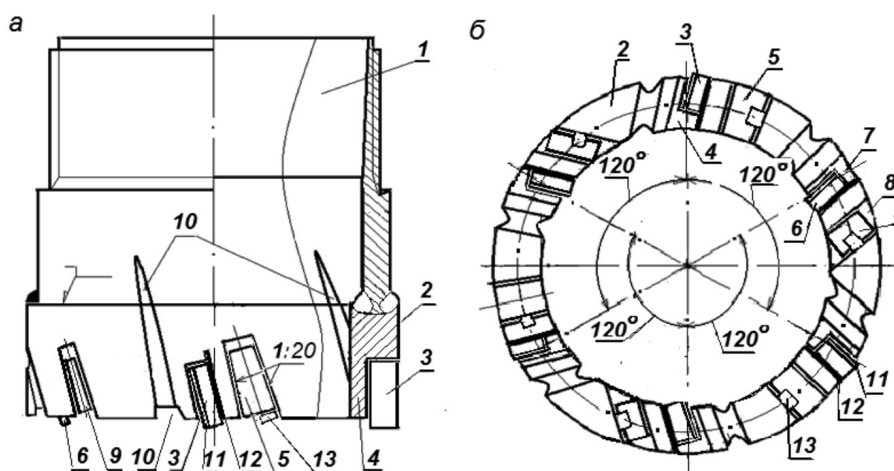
Общий вид спереди а) и снизу б) на буровую коронку с пайокклиновым креплением резцов: 1 – корпус коронки; 2 – корончатое кольцо; 3 – резец скважинообразующий; 4 – боковая стенка паза под скважинообразующий резец; 5 – клин скважинообразующего резца; 6 – кернообразующий резец; 7 – боковая стенка паза под кернообразующий резец; 8 – паз под клин 9; 9 – клин под кернообразующий резец; 10 – пазы и каналы промывочные; 11 – сверхтвердый слой резца; 12 – шов пайки ленточным припоем; 13 – стопор
